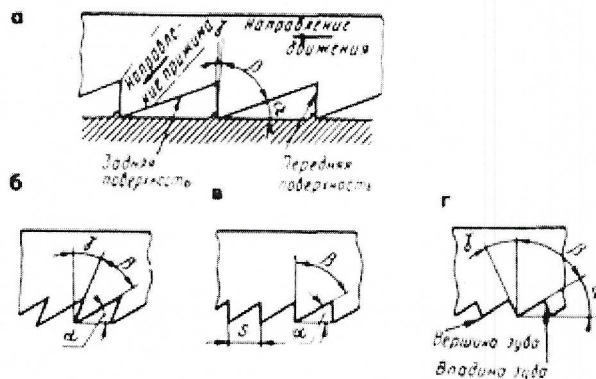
Элементы зуба ножовочного полотна (а); передний угол зуба положительный (б), равный нулю (в) и отрицательный (г)
